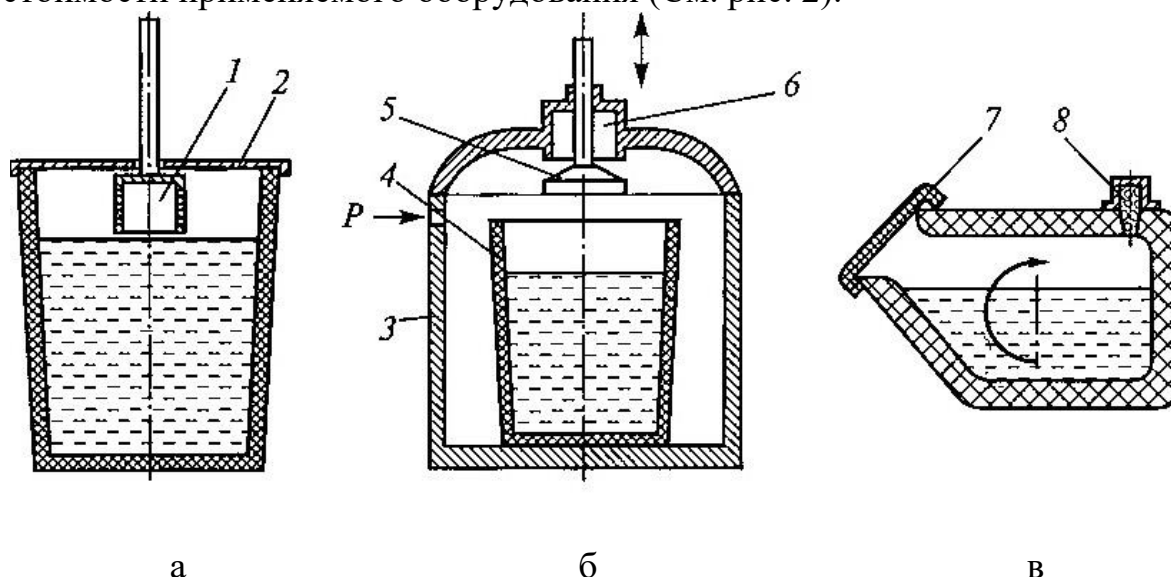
Способы ввода в расплав сфероидизирующих модификаторов: а — под колокольчиком; б — в автоклаве; в — в герметизированном ковше-конвертере; 1 — колокольчик; 2 — крышка; 3 — корпус автоклава; 4 — ковш с металлом; 5 — мешалка; 6 — полость для модификатора; 7 — крышка ковша; 8 — модификатор
